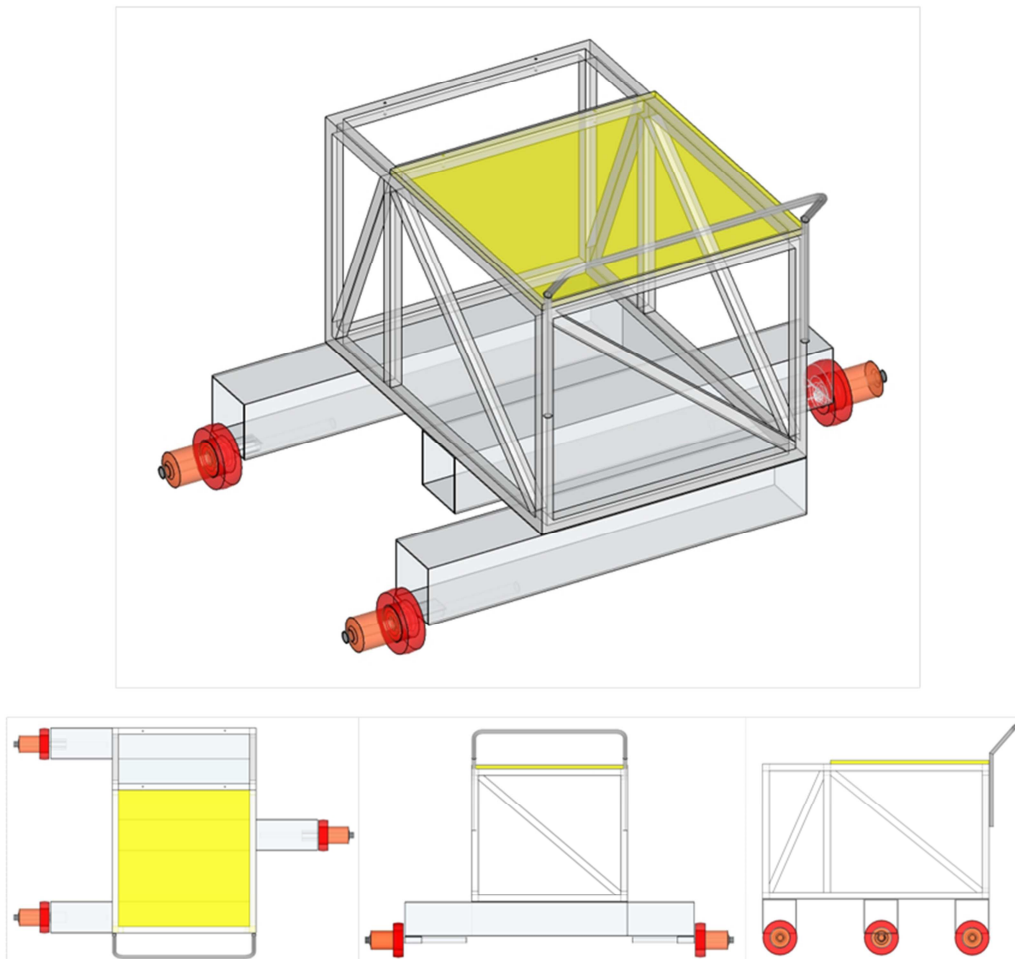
Diseño del prototipo de inspección de túneles ferroviarios
